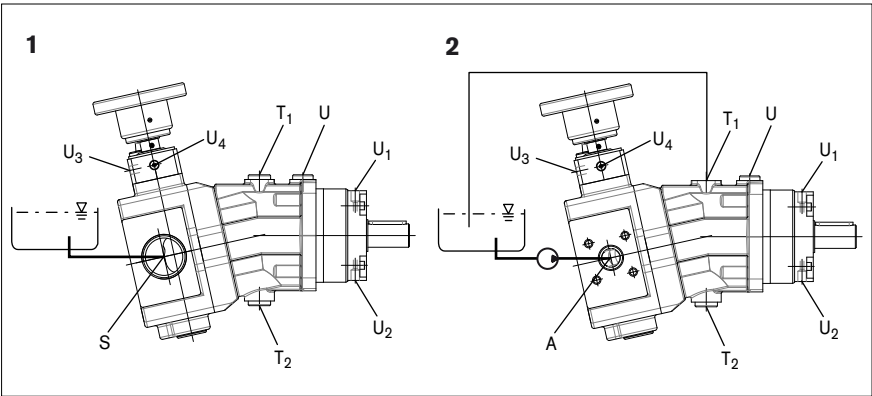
Einbaulage 1: offene Bauart, Einbaulage 2: geschlossene Bauart
